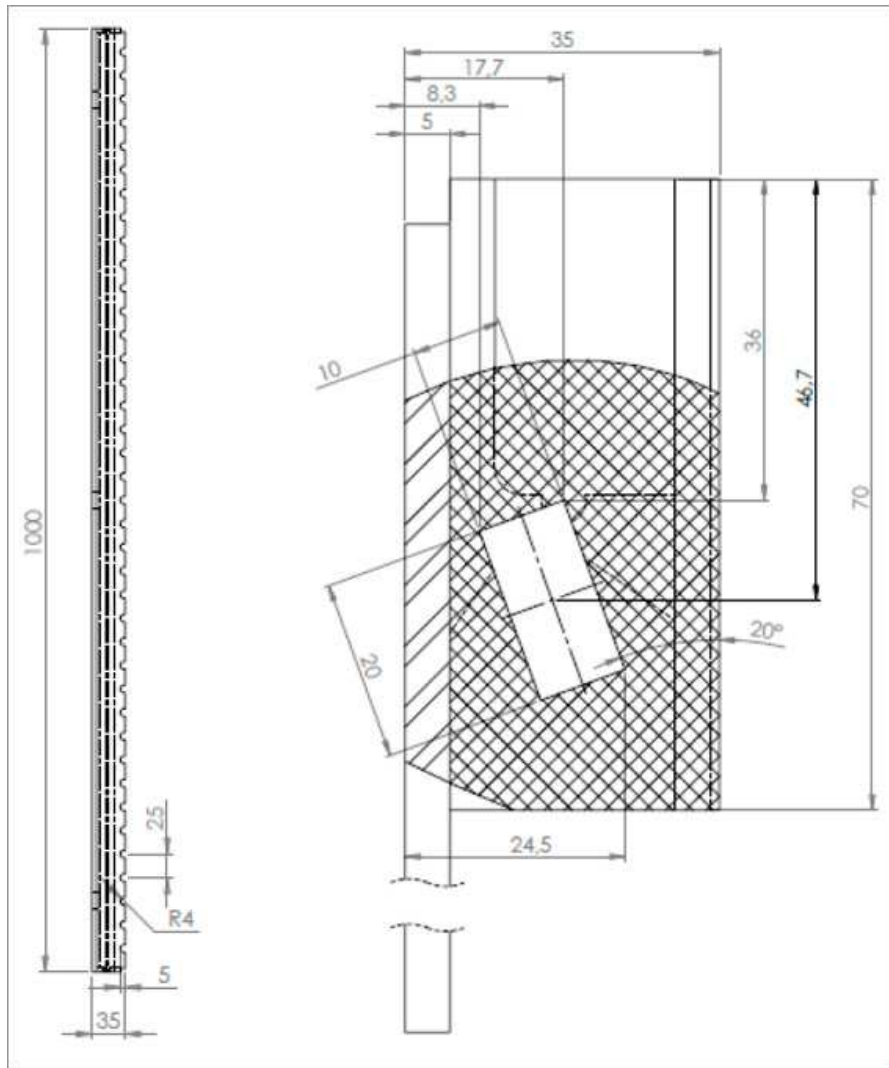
Vista em planta e vista em perfil do Gap Filler monolítico de 35mm
